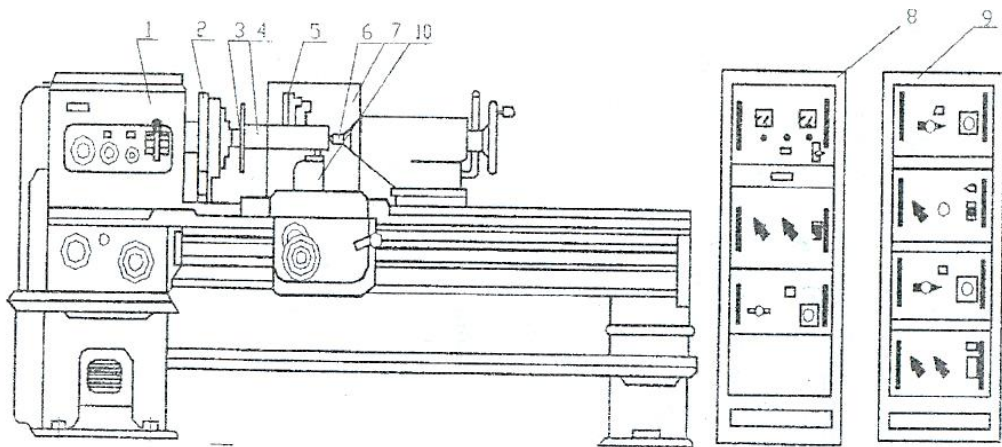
Схема установки «Елітрон-344»: 1 – токарний верстат 1К62; 2 – трикулачковий патрон з струмознімачем; 3 – оправка; 4 – оброблювана деталь; 5 – обробна головка; 6 – центр; 7 – екран; 8, 9 – генератори; 10 – обкатник
